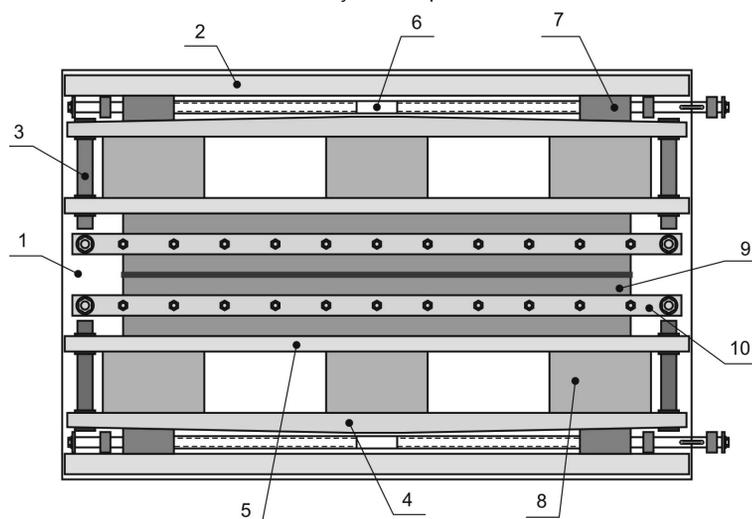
Конструкция технологической оснастки для сварки плоских образцов
